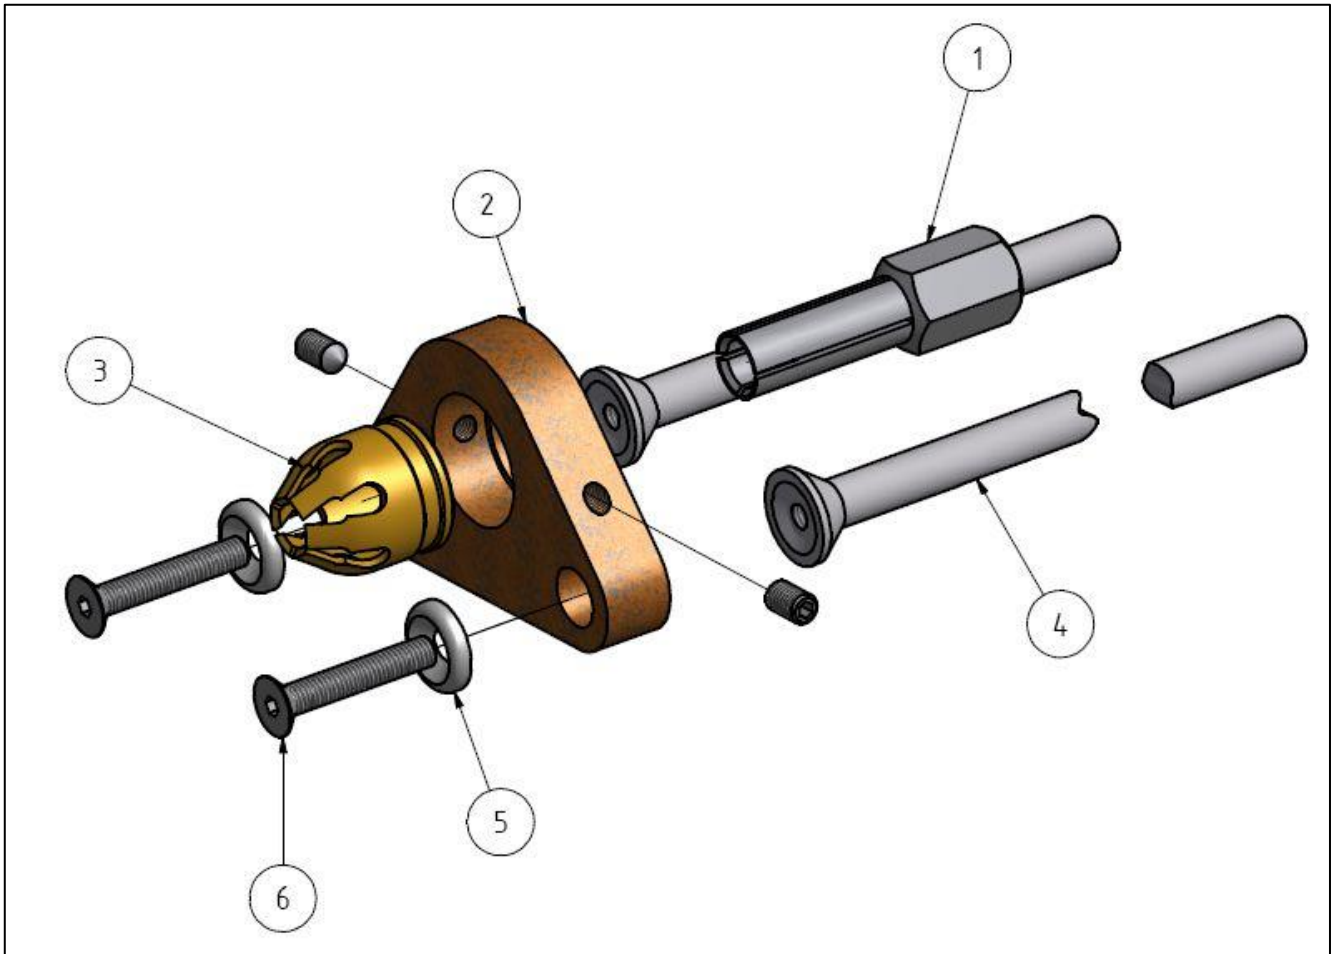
Stützeinrichtung für Gewindebolzen und glatte Stifte
